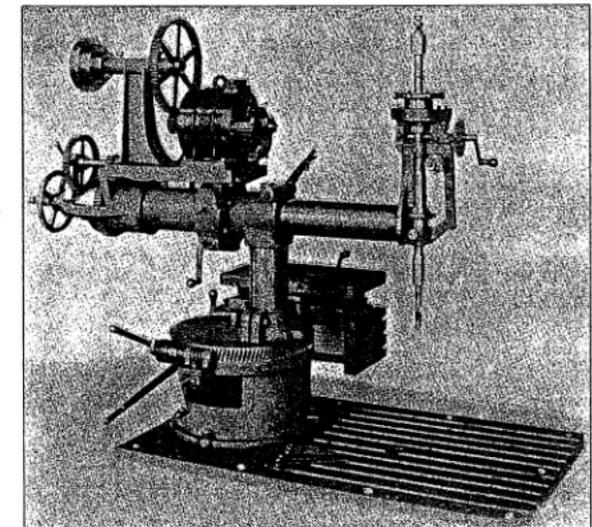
/5: Universal-Radialbohrmaschine (um 1898) Patent Michaelis mit elektrischem Einzelantrieb und Spannfläche auf Bodenniveau
